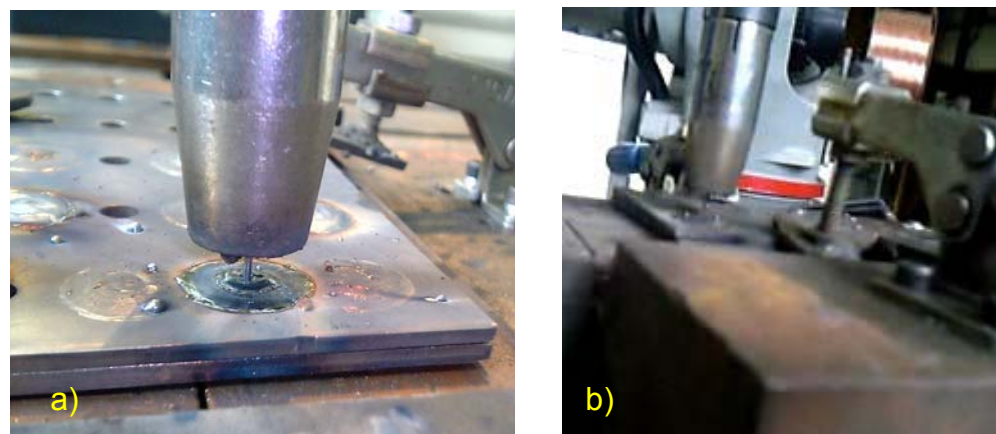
Ponta do arame ao final da solda: a) arame grudado na solda; b) ponta do arame livre, pronta para a próxima solda.
